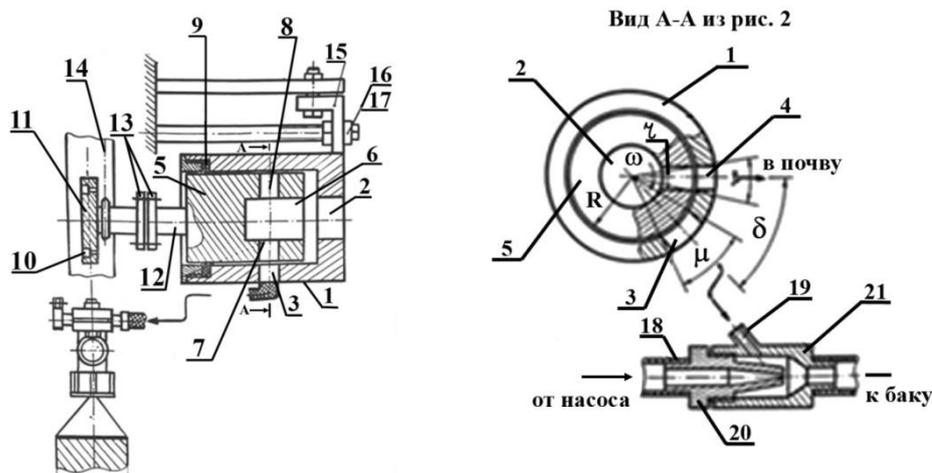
Схема приспособления для локального (гнездового) внесения гербицидов:
